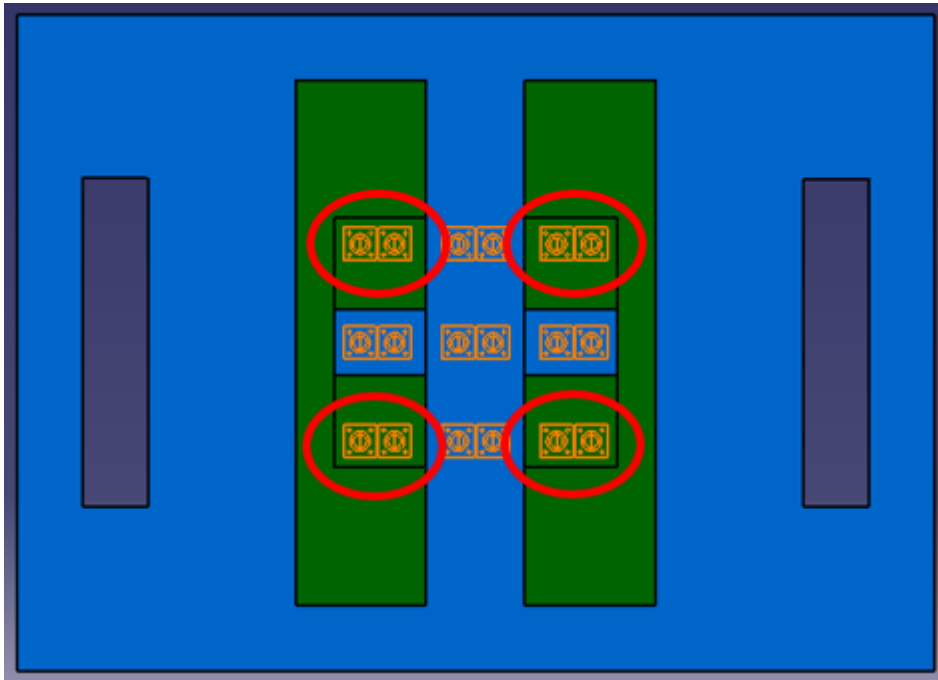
Vista inferior da ferramenta (Fonte – Construção própria)
